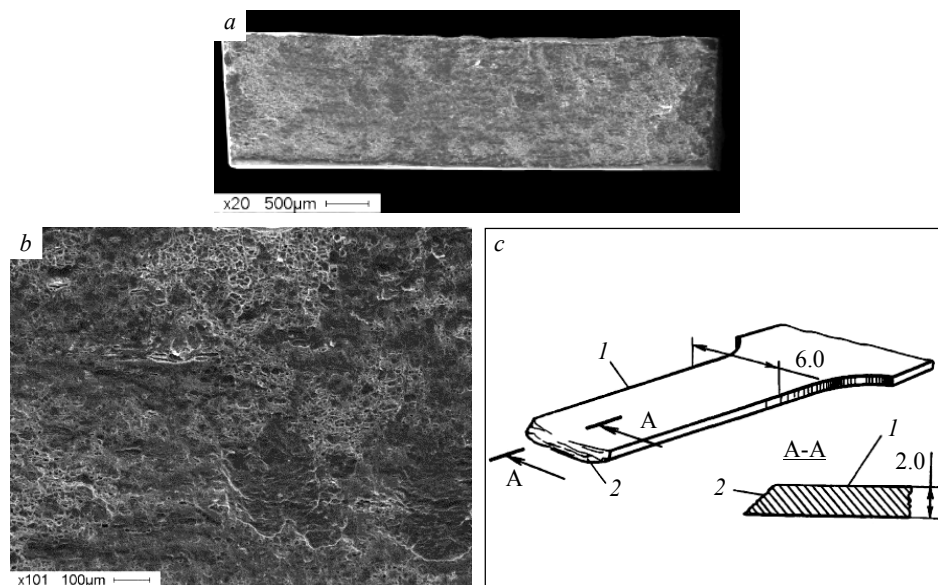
Поверхность излома образца из прокатанного алюминиевого сплава группы 4 без добавления частиц и без обработки УЗ: *a* – общий вид поверхности разрушения, *b* – типичный вид излома; *c* – схема косого излома плоского стального образца, разрушившегося в результате среза при растяжении [27]. В этом случае разрушение произошло вдоль направления действия максимальных касательных напряжений: *1* – образец после испытания на растяжение; *2* – поверхность излома
